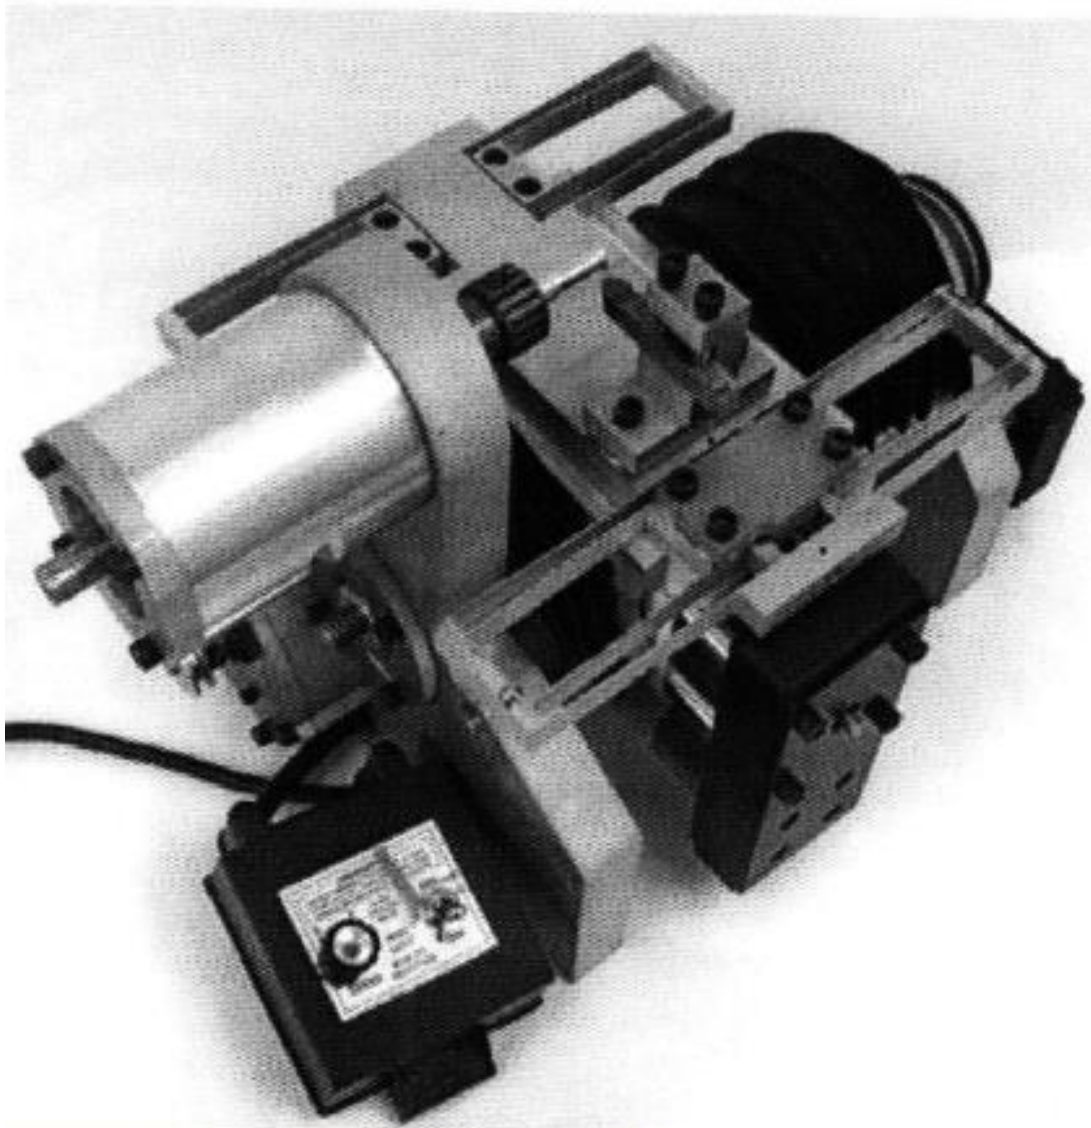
Модернизированный настольный токарный станок с ЧПУ
